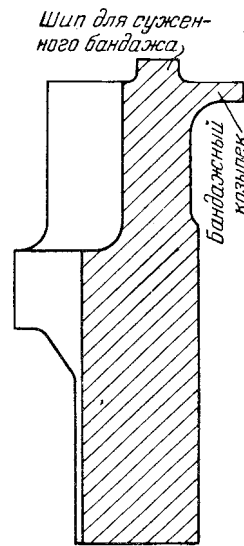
Лопатка с фрезерованным заодно бандажем.
